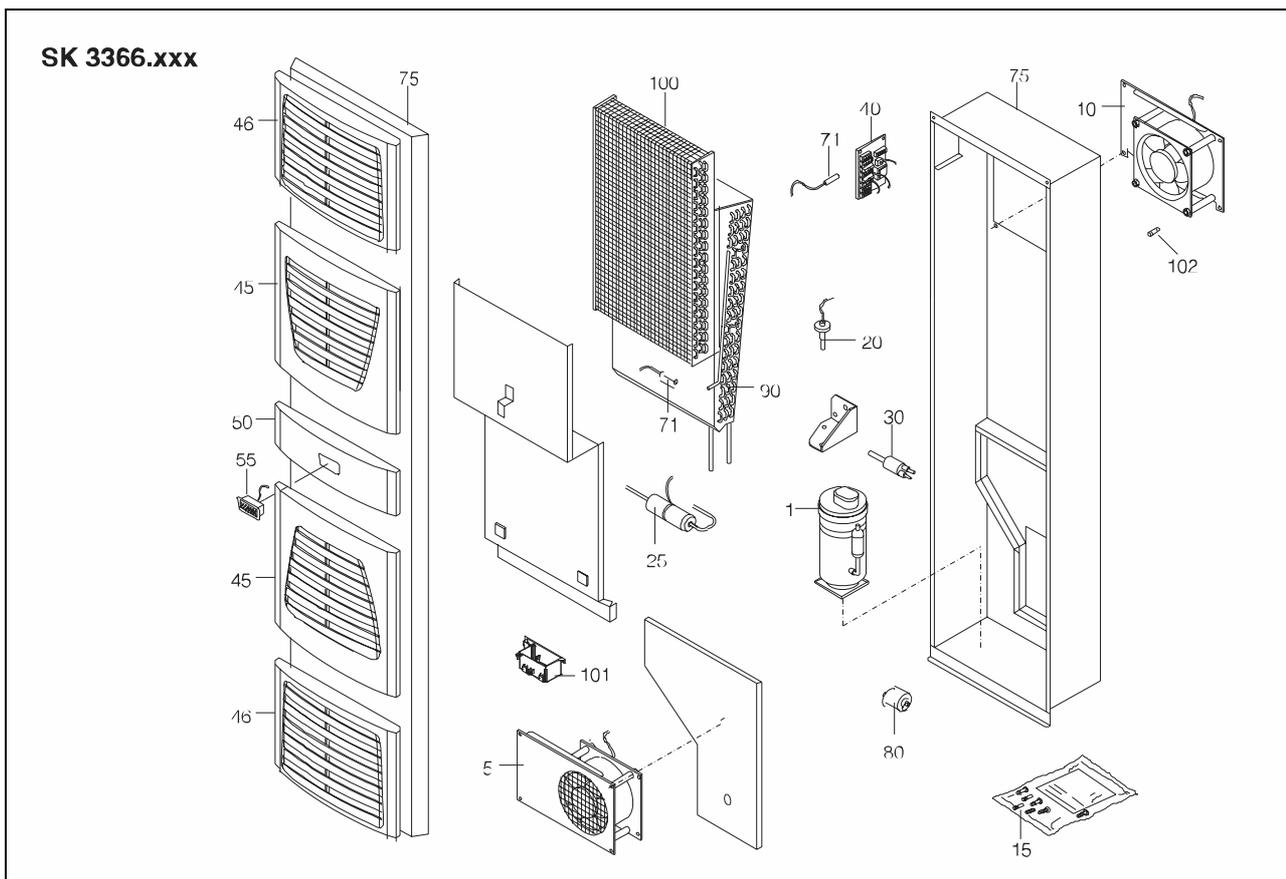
Pièces de rechange pour SK 3366.xxx
